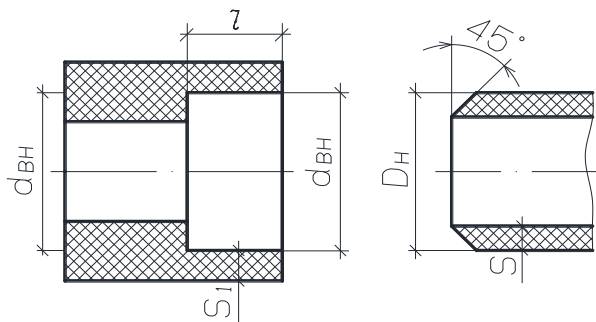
Конструктивные элементы подготовленных кромок (швы НС3 и НС4)
